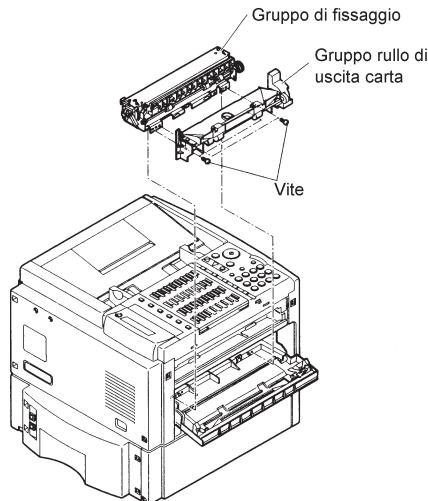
Procedura di smontaggio (Gruppo di fissaggio)
